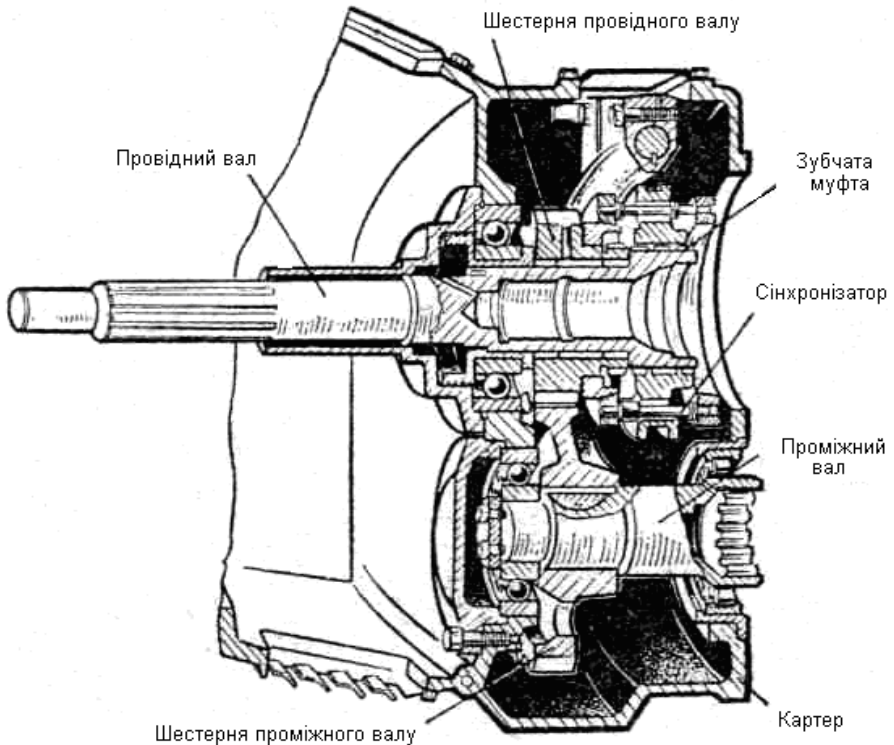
Деталі коробки передач автомобіля КамАЗ
